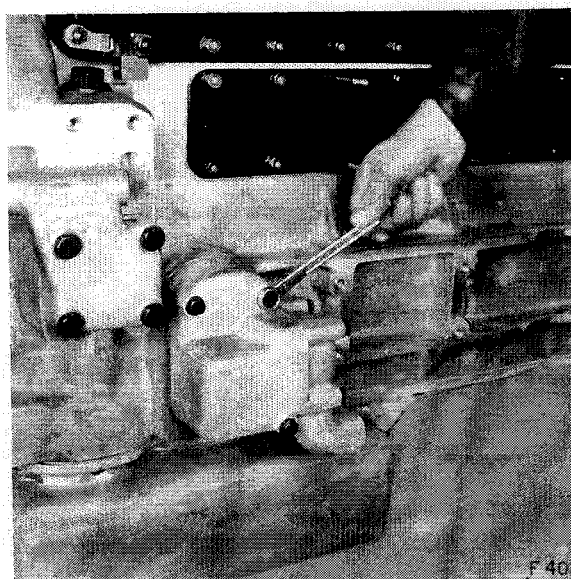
Lösen der Befestigungsschrauben am Belüfter für das Kurbelgehäuse
